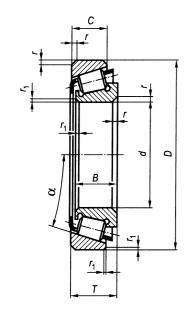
Подшипник роликовый радиально-упорный конический однорядный
